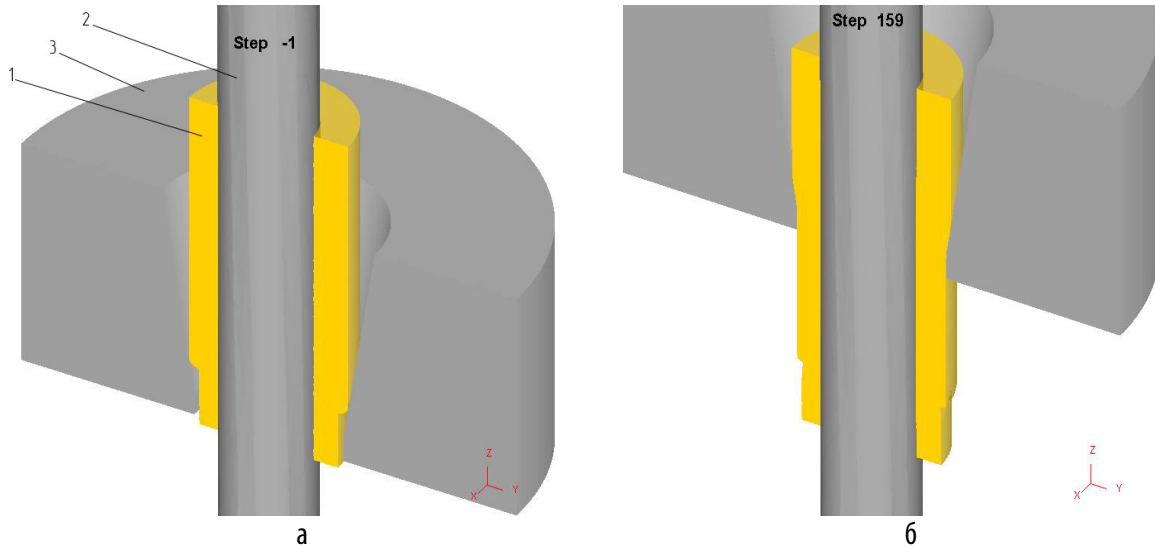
Расчётная схема процесса: а – исходное положение; б – в момент установившейся стадии
